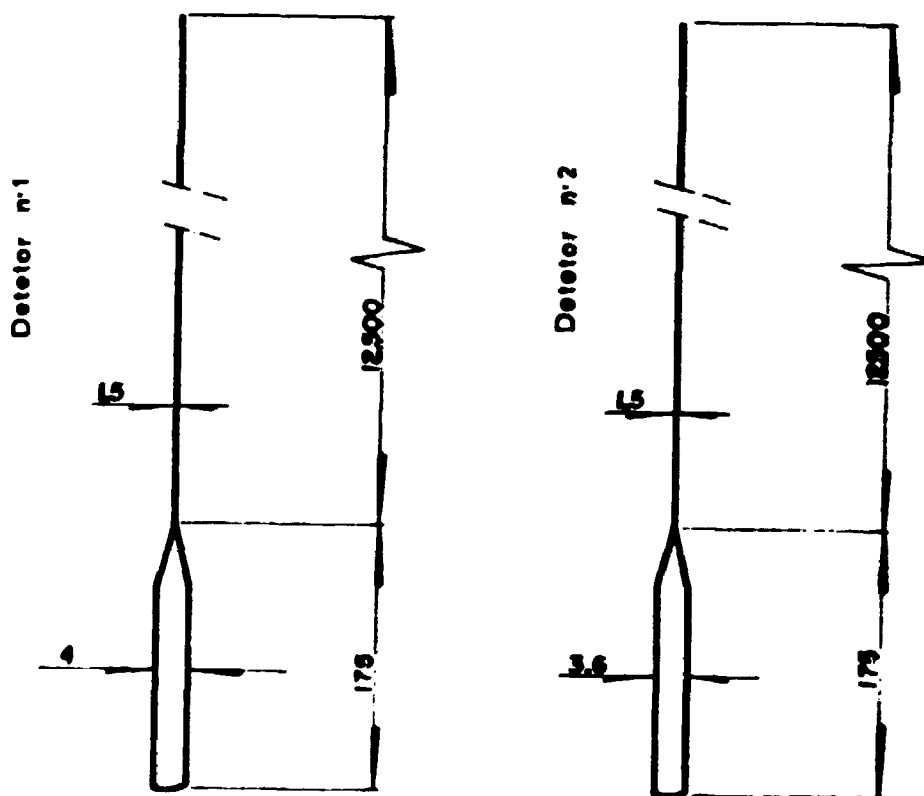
Detetores SPND utilizados (dimensões em mm).
